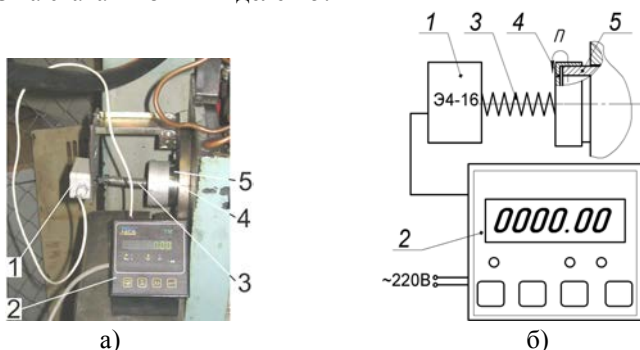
Загальний вигляд а) та принципова схема визначення частоти обертання шпинделя б): 1 – енкодер; 2 – електронний тахометр; 3 – пружина; 4 – стакан, 5 – шпиндель
